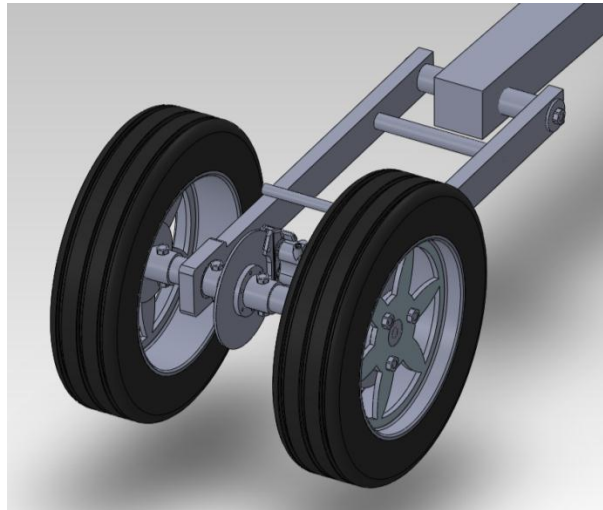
Montagem com eixos, motor, disco e pinça de travão
